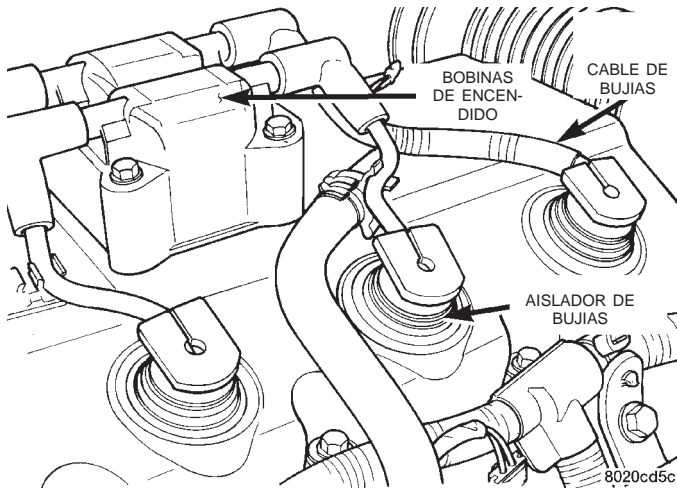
Conjunto de bobina de encendido electrónico—motor de 2.0L
